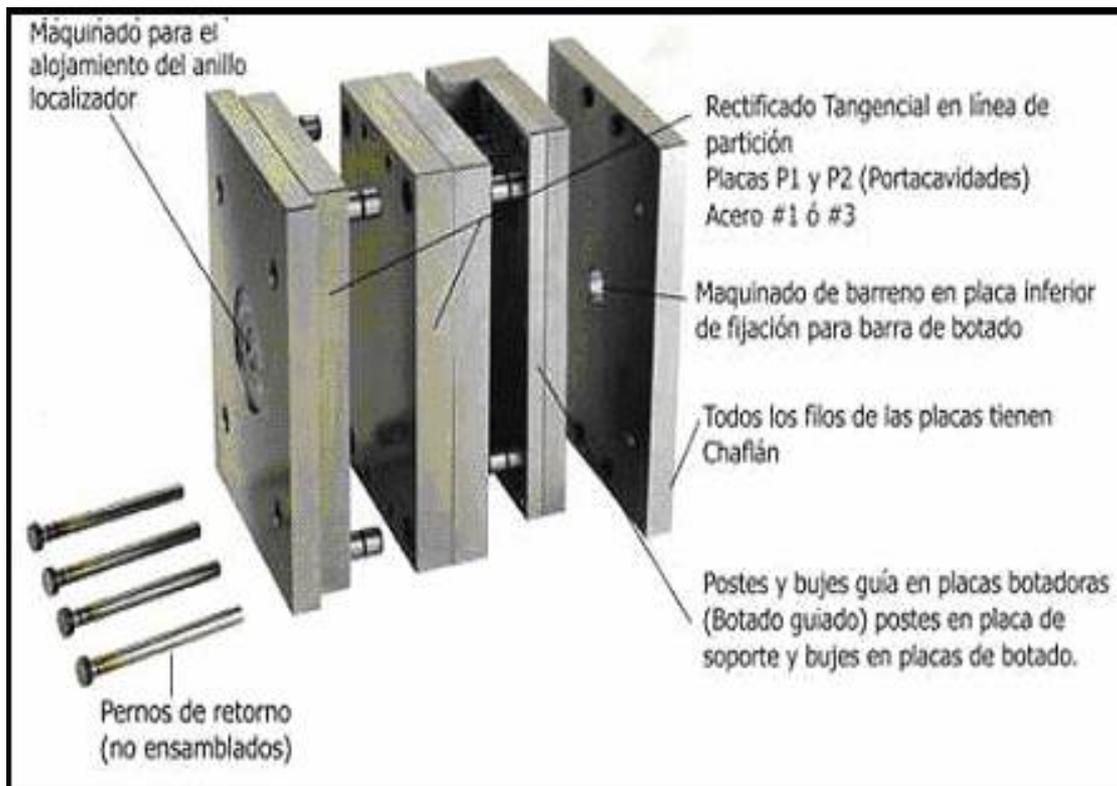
Ensamble porta molde propuesto por proveedor Polimold S.A. DE C.V.
